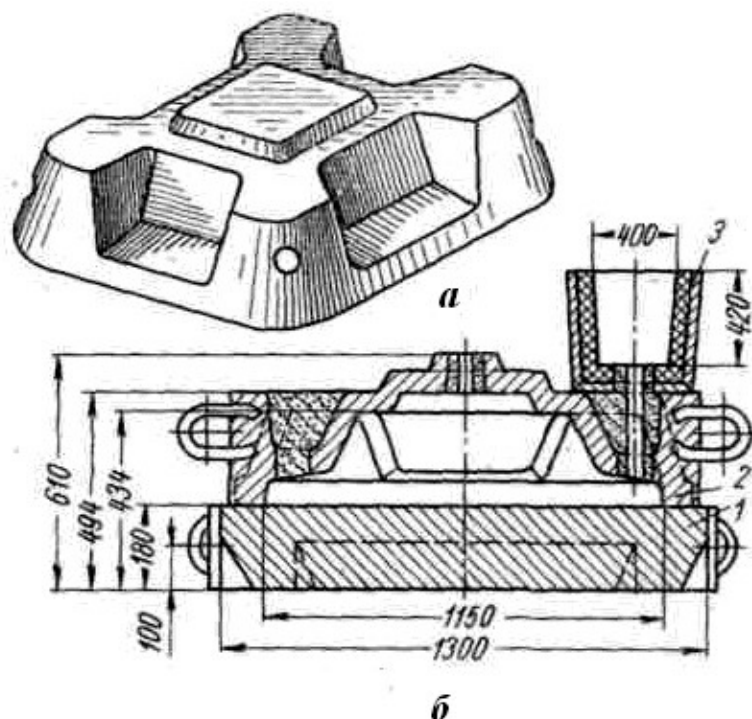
Одноместный поддон (а) и кокиль для его отливки (б)
